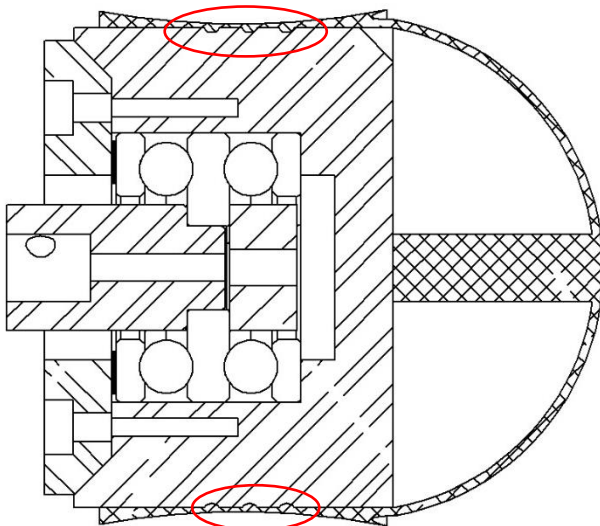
Vue en coupe de la tête de piston. Détails en annexe 6
